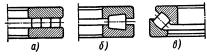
Роликоподшипники упорные: а—с цилиндрическими роликами, тип 9000; б—с коническими роликами, тип 19000, ГОСТ 5380—50; в—со сфероконическими роликами, тип 39000, ГОСТ 9942—62
